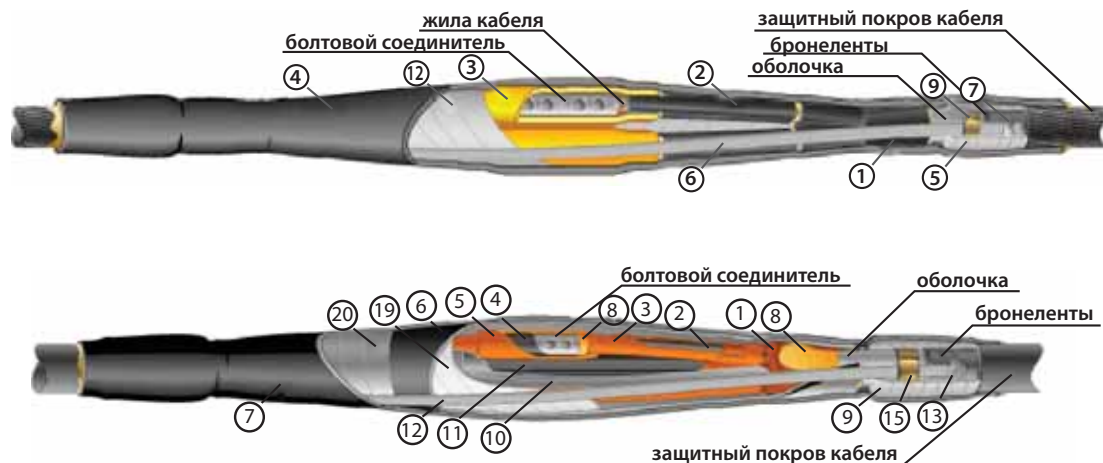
Кабельная соединительная муфта на основе термоусаживаемых материалов для 3-х жильного кабеля на напряжение 6 и 10 кВ.
